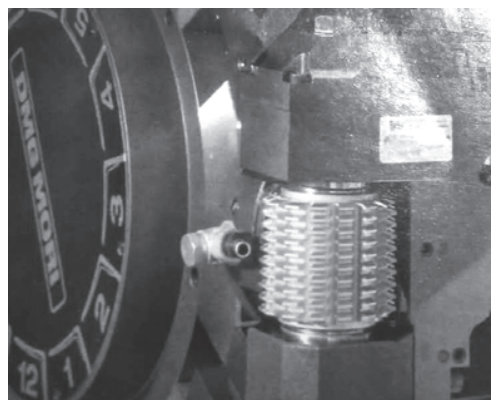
Зубообработка с помощью блоков GEARHOBGINGUNIT
